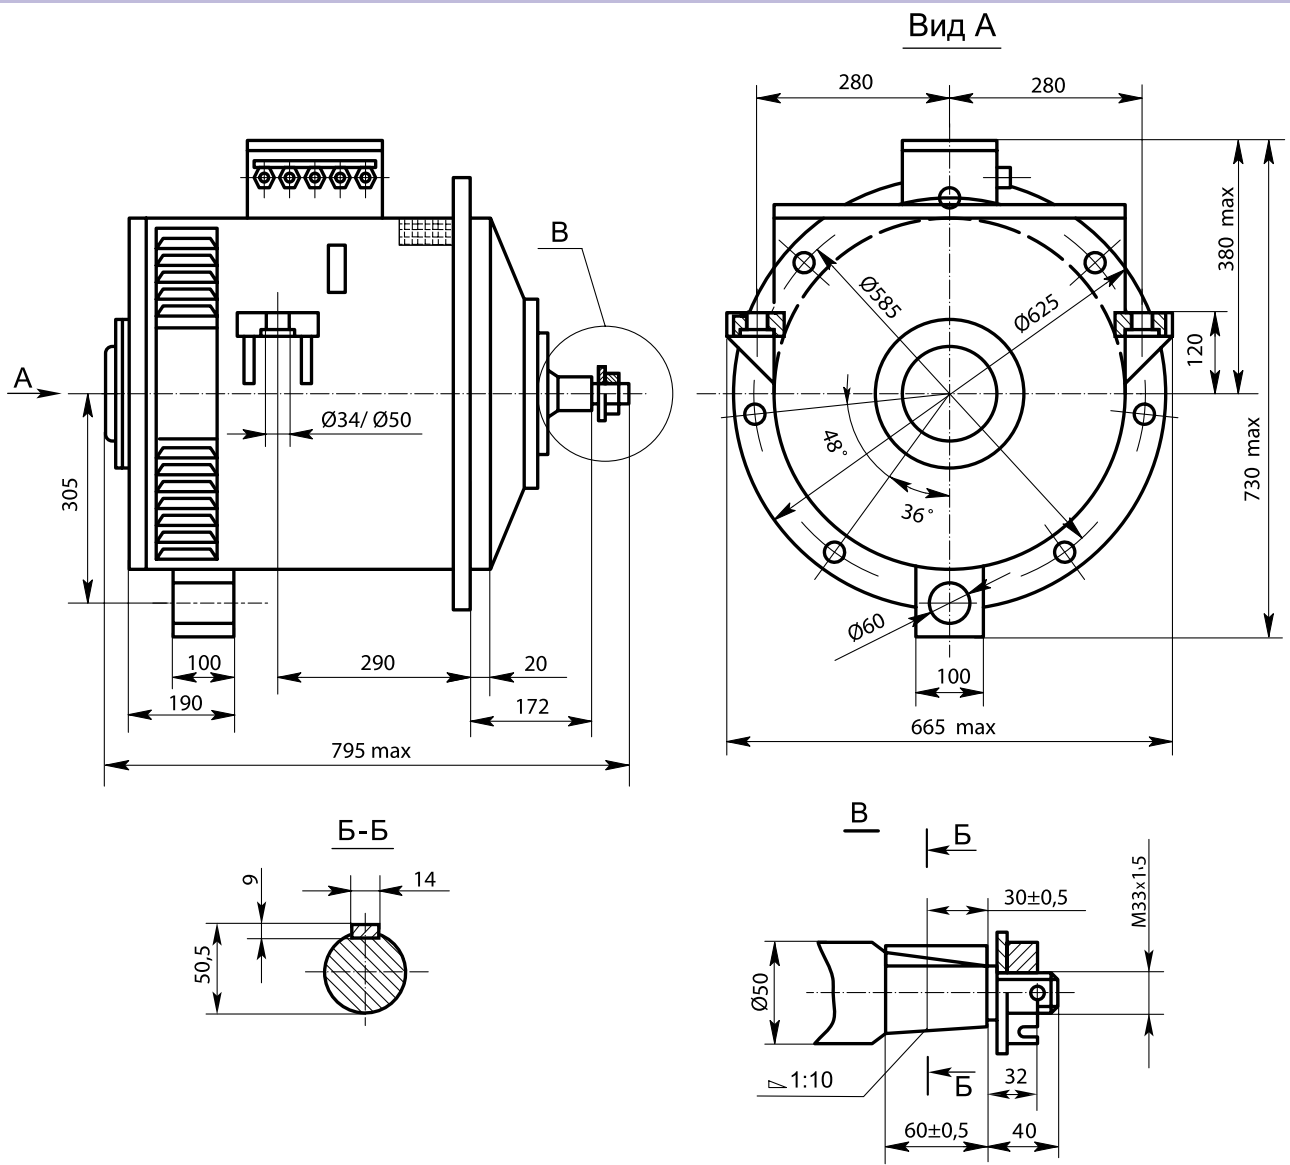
Габаритные и установочные размеры электродвигателя ДТН-46/33М
